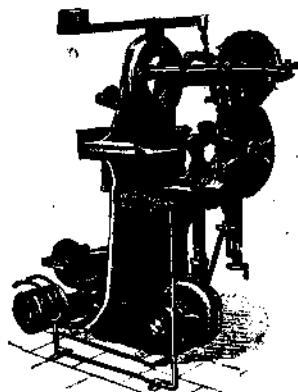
Усовершенствованный наждачно-точильный станок для круглых и ленточных пил.
